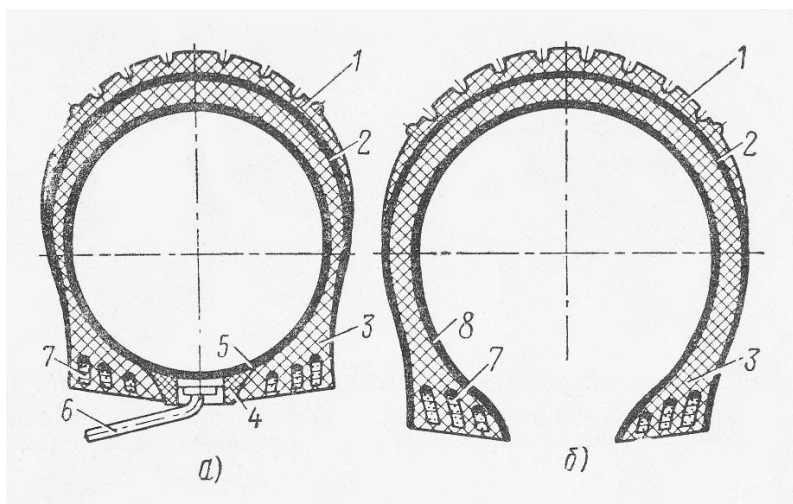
Конструкція камерного(а) і безкамерного пневматиків(б):
